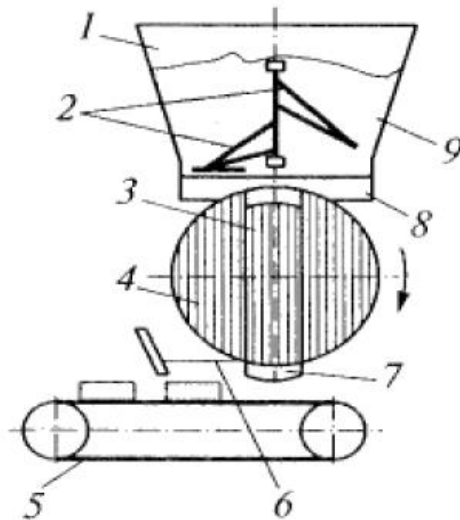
Схема барабанної машини для формування котлет: 1 – бункер; 2 – лопатевий нагнітач; 3 – поршень; 4 – формувальний барабан; 5 – транспортер; 6 – струнний механізм; 7 – виріб; 8 – живильник; 9 – фарш
